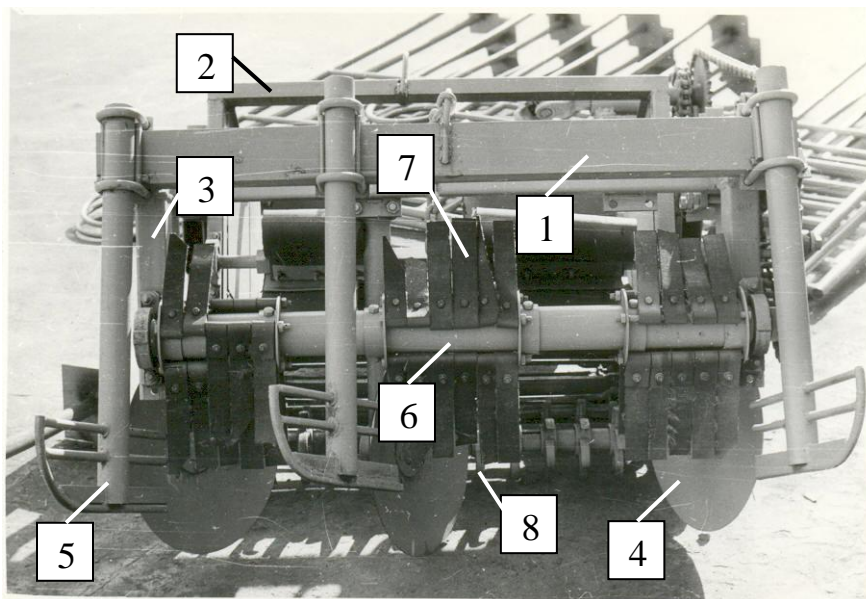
Загальний вигляд викопуючого пристрою: 1 – рухома рама; 2 – основна рама; 3 – стояк сферичного диска; 4 – сферичний диск; 5 – корененапрямник; 6 – очисний вал; 7 – пружні очисні лопаті; 8 – розрихлювач
